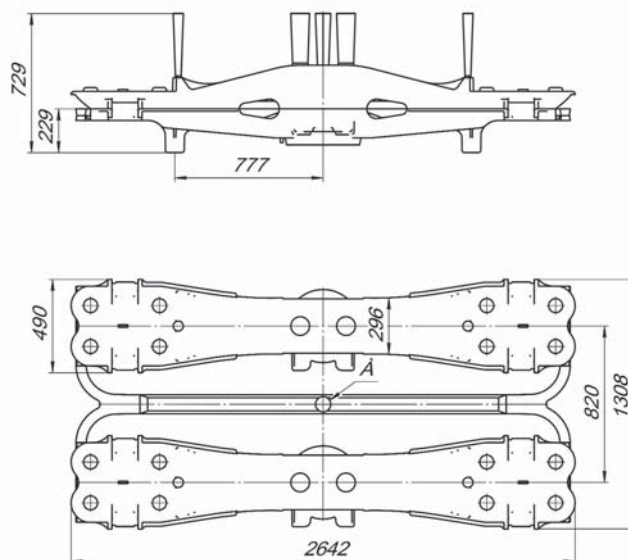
Схема куста отливок «Балка наддрессорная» модели 100.00.001-6
